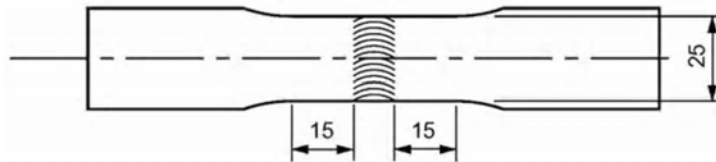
Probeta para el ensayo de tracción perpendicular a la soldadura
